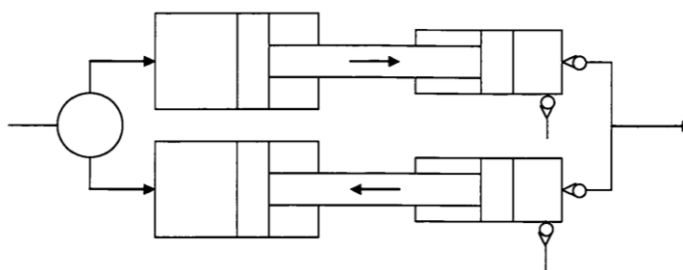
Schéma stroje pro řezání vodním paprskem [16]
